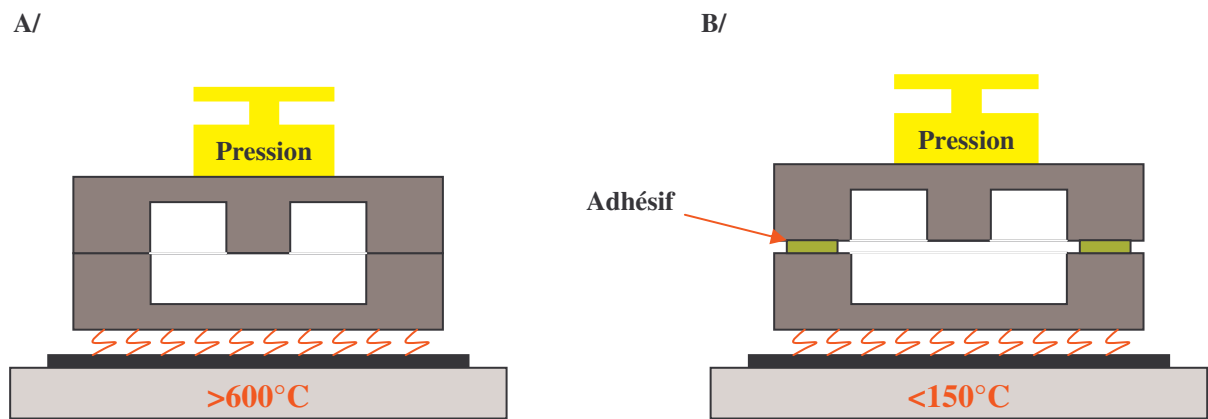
Types de soudure. A/ thermique ; B/ adhésive.
